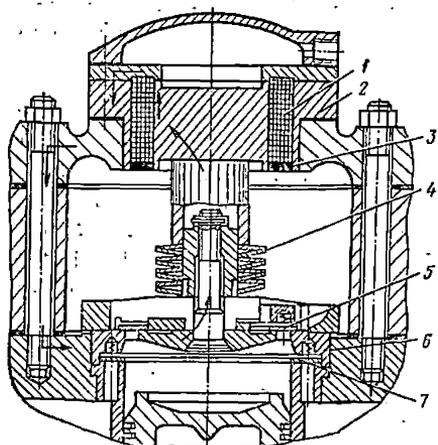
Клапанная группа компрессора П110 с электромагнитным отжимом пластины всасывающего клапана: 1 — катушка; 2 — корпус катушки; 3 — втулка магнитопровода; 4 — буферная пружина; 5 — клапан нагнетательный; 6 — корпус всасывающего клапана; 7 — пластина
